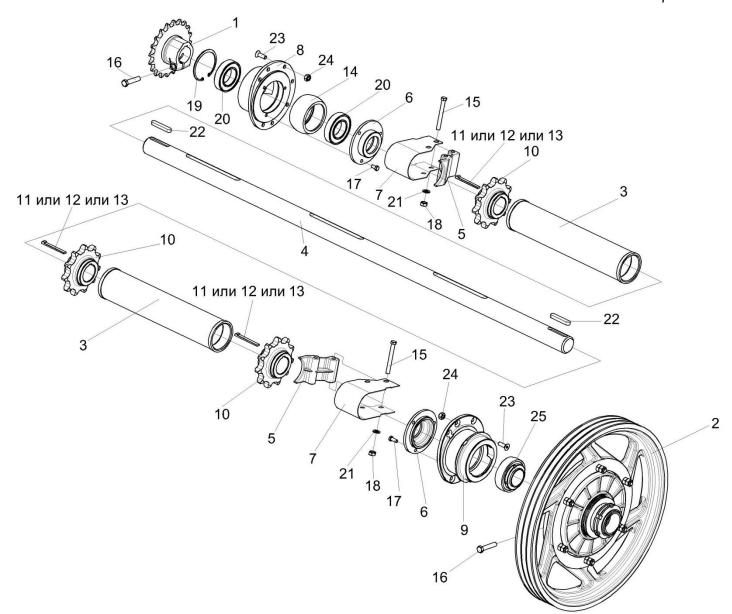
Установка вала верхнего КЗК-8-1813000
